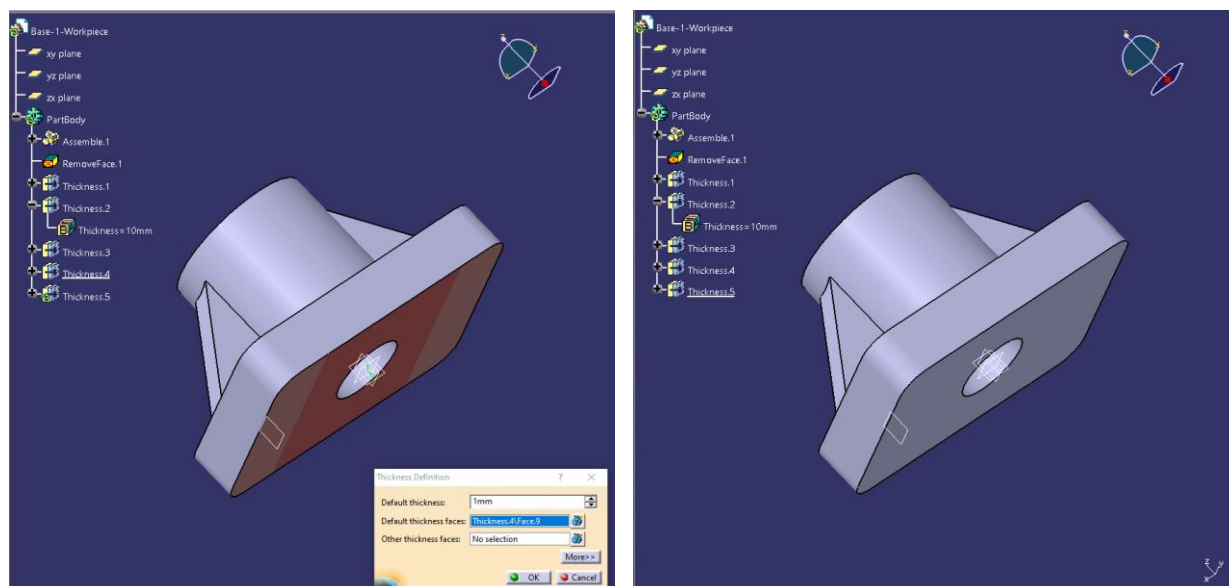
Трехмерная модель заготовки, изометрический вид
